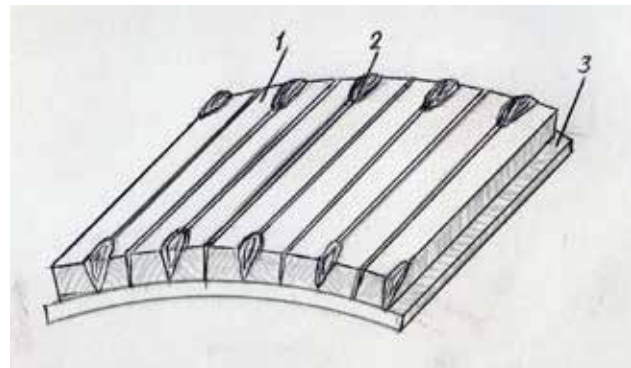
Схема збірки і плазмового зварювання стрижнів
